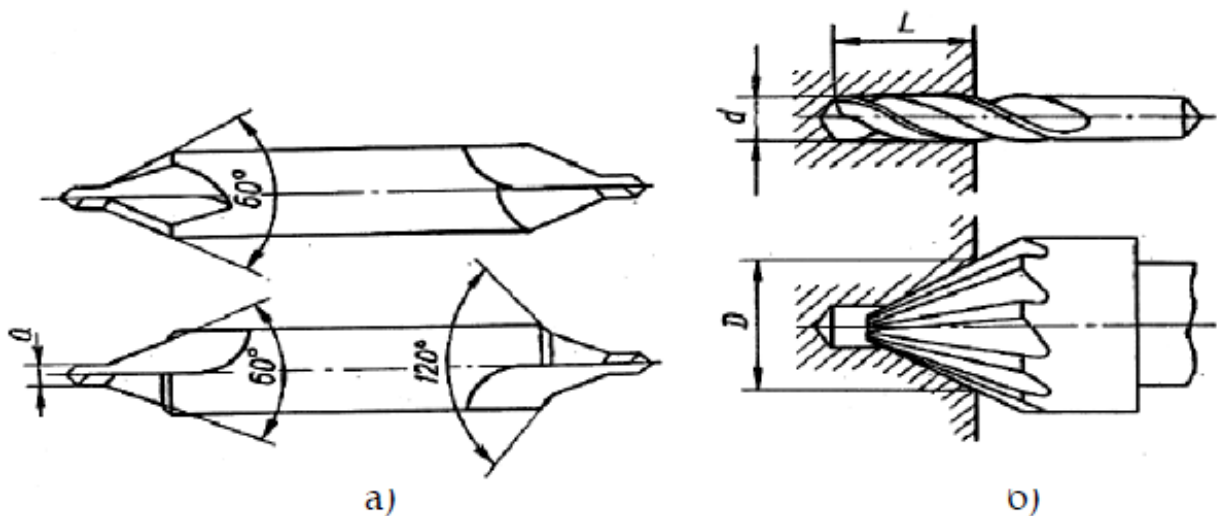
Виготовлення центрального отвору а - центровими свердлами; б - двома інструментами
